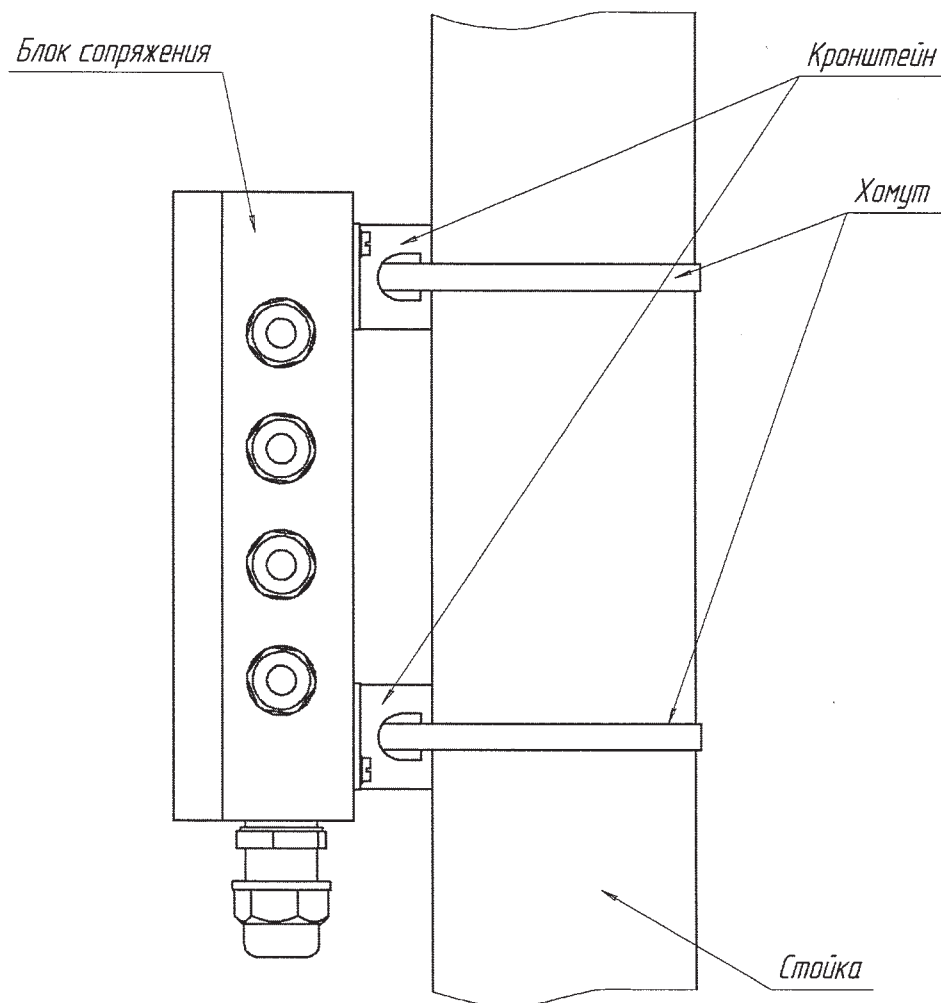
Внешний вид блока сопряжения, установленного на опоре
